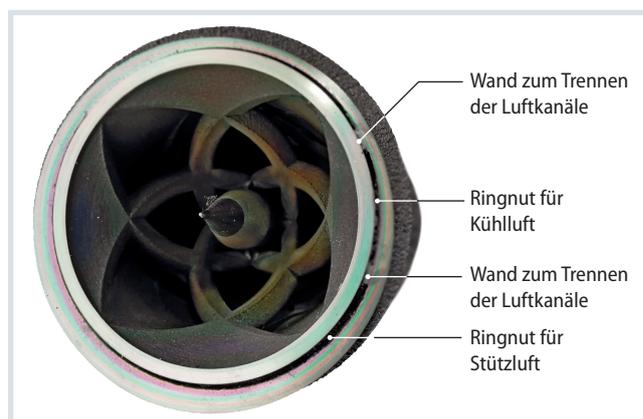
Stirnseite des Mischschlauchkopfs mit der durch zwei Wände geteilten Ringnut, über die sowohl die Stütz- als auch die Kühlluft vom Flansch in den Kopf überführt wird
